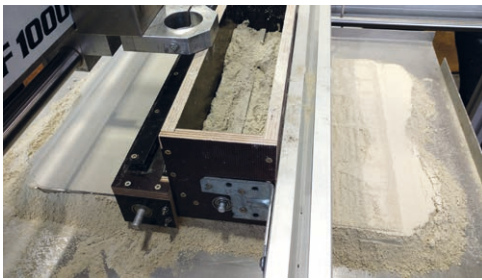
Dispenser für die Herstellung der Materialschicht; rechts: frisch aufgetragenes Material, links: geglättete und verdichtete Schicht | Fig. 3: Dispenser for creating dry material layers; right: freshly dispensed material, left: smoothed and compacted layer
